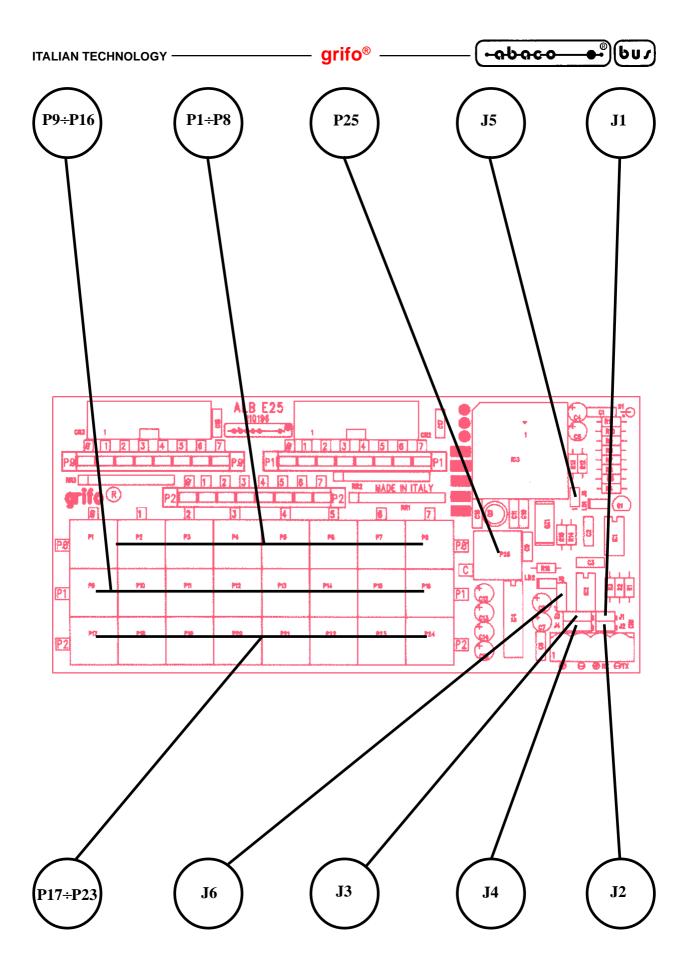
DISPOSIZIONE PULSANTI E JUMPERS SULL'ALB E25
